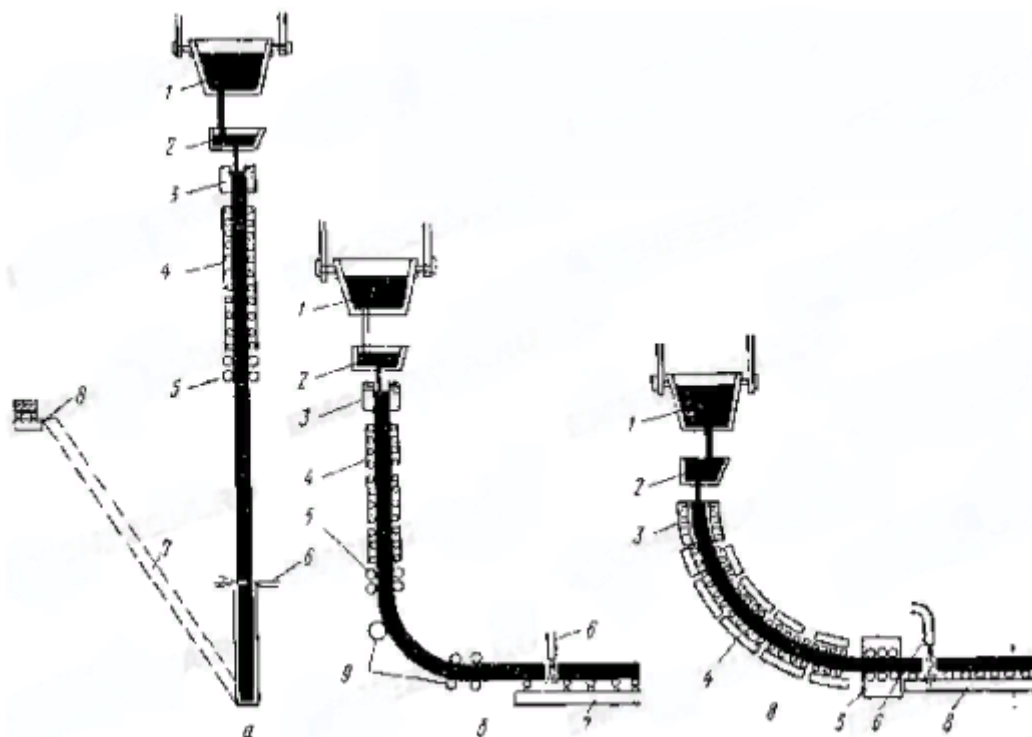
Машина непрерывного литья заготовок (МНЛЗ)[10]:
